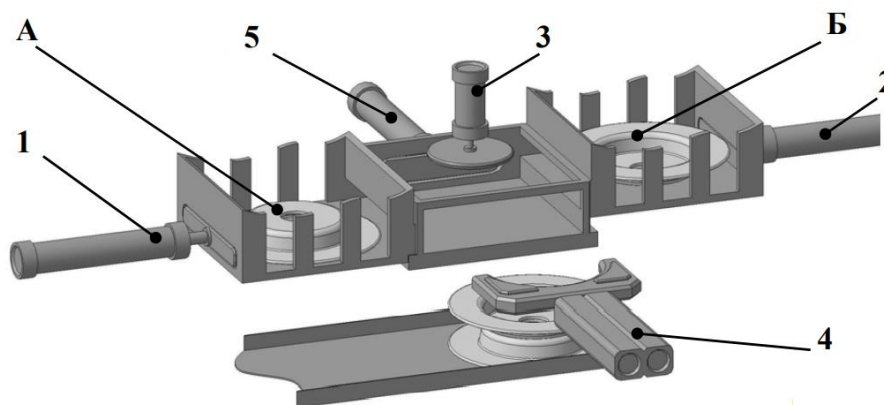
Конструктивна схема маніпулятора зварювальної станції
